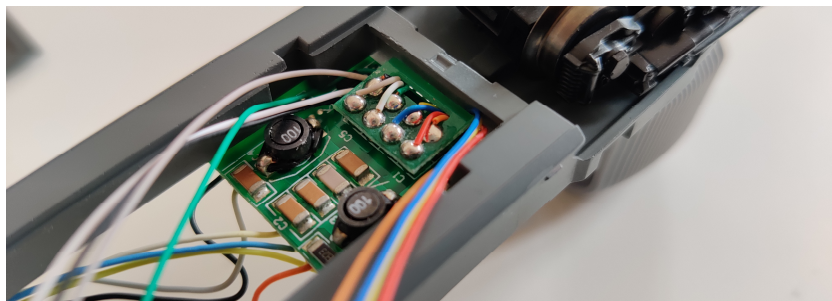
Korrekte Einbaurichtung des Schnittstellen-Steckers in Piko H0-Modelle
